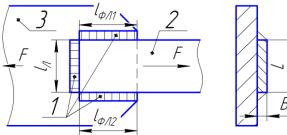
Схема сварочного соединения листов внахлест Заклепочные и шпоночные соединения рассчитывают как на срез, так и на смятие.
